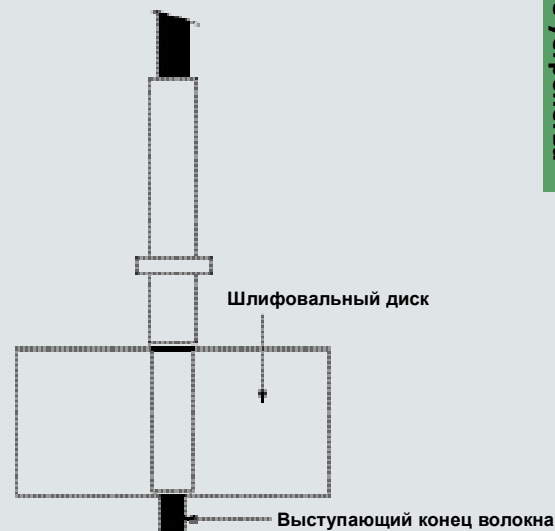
Шлифовальный диск с направляющей для втулки разъема
